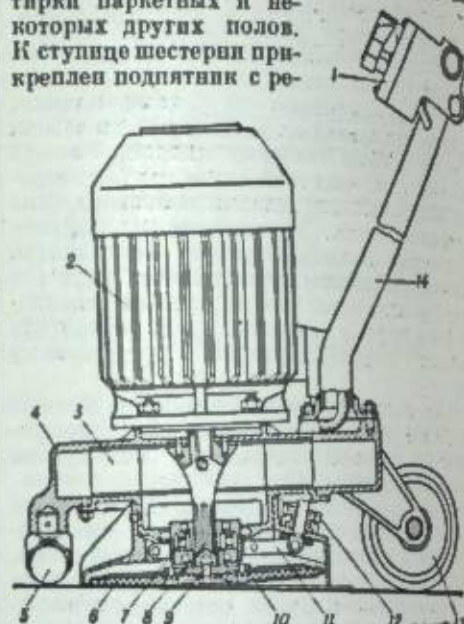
Паркетшлифовальная машина С-662: 1 — включатель; 2 — электродвигатель; 3 — крыльчатка вентилятора; 4 — корпус; 5 — передняя опора; 6 — рабочий диск; 7 — шлицевая втулка; 8 — шлицевой вал; 9 — крепежный винт; 10 — шлифовальный диск или шкурка; 11 — хомут регулирующего устройства; 12 — регулирующая гайка; 13 — ходовое колесо; 14 — рукоятка.
